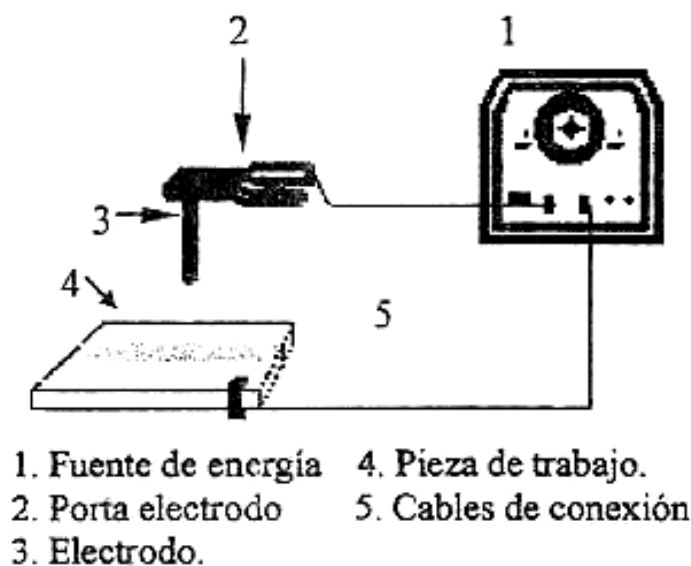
Equipo para el proceso de soldadura por arco metálico protegido
